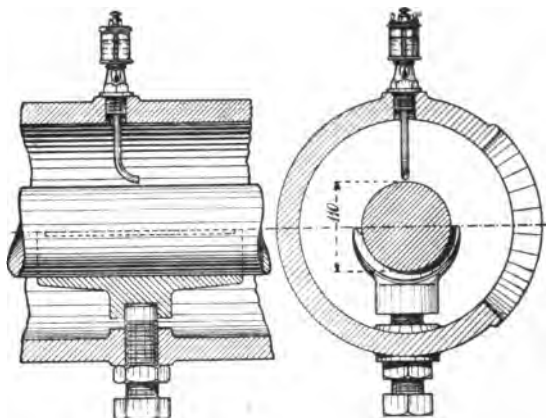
216. Schmierung der Kolbenstange für Tandemmaschinen (im Verbindungstück der beiden Cylinder.)
